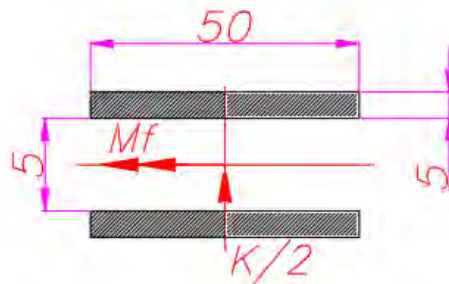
Fuerza de corte sobre garganta de soldadura – Escenario 1.
